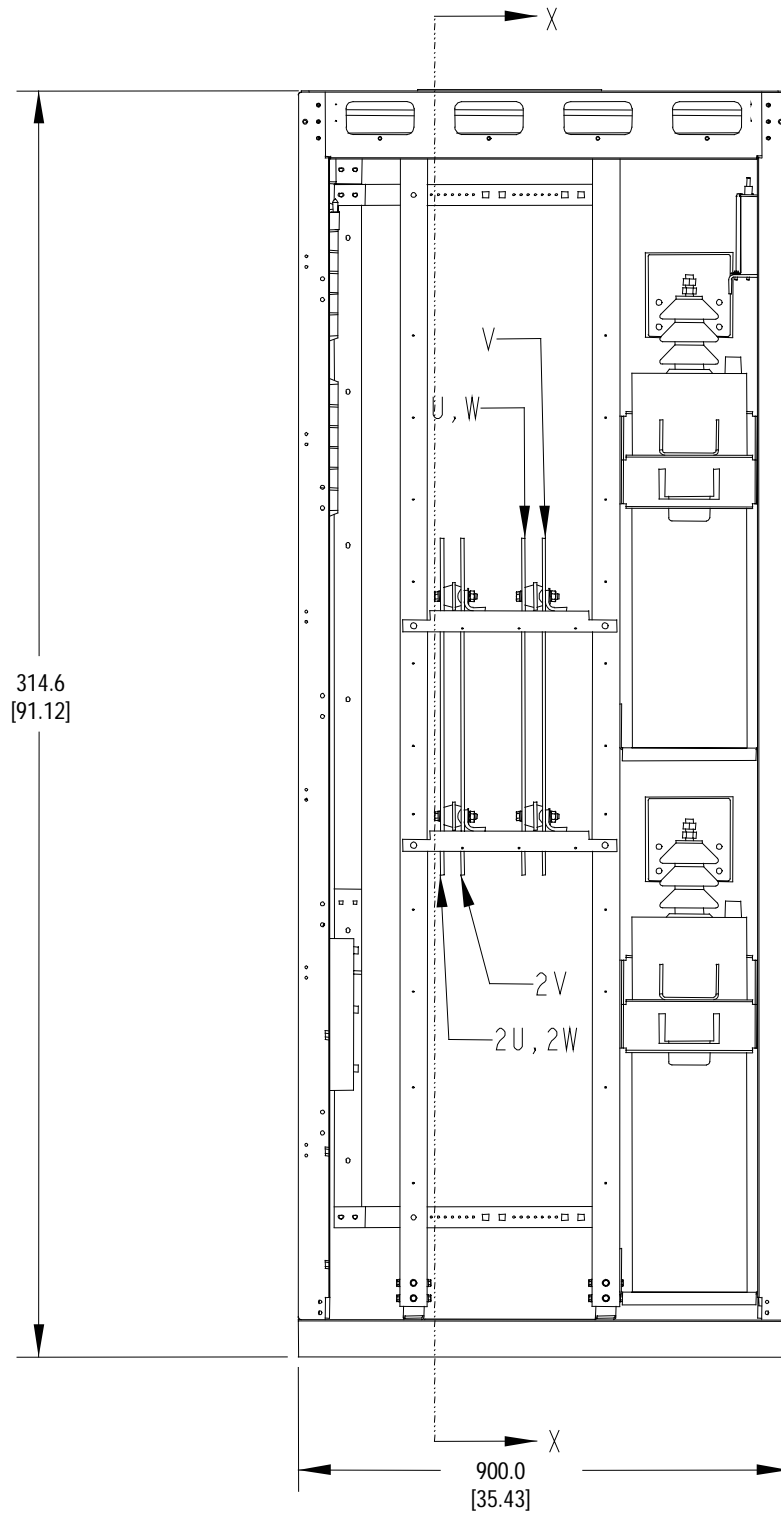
Frontansicht des 900 mm Anschlußschaltschranks
